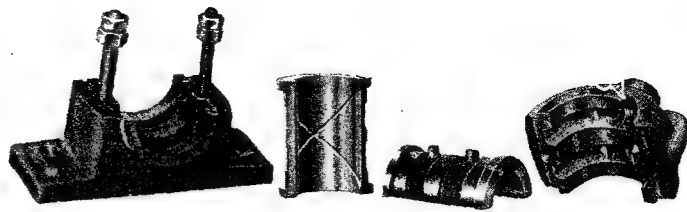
Despiece del soporte representado en la figura anterior.
